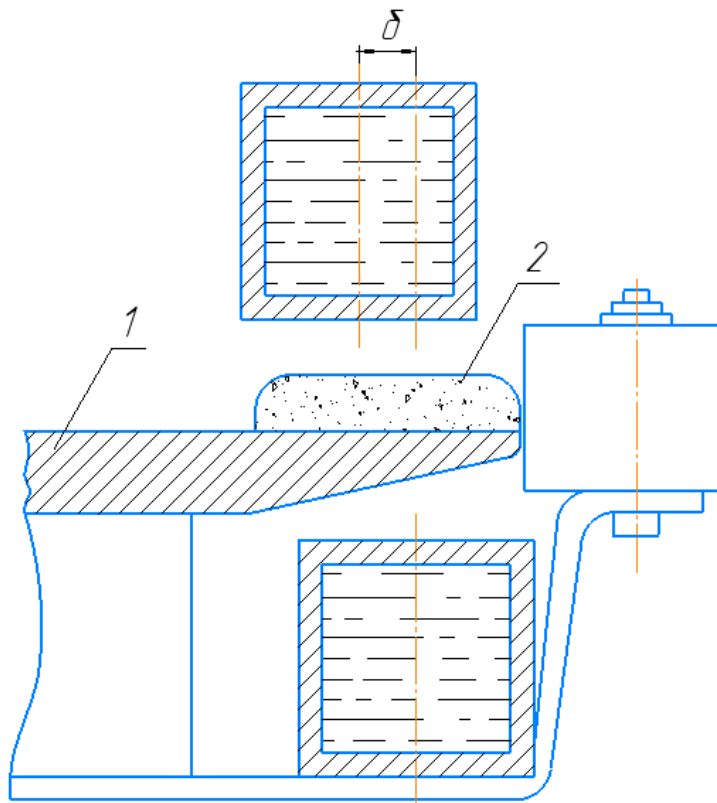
Положення лапи культиватора в індукторі при наплавлюванні: 1- деталь; 2- шар шихти [8 ст.151]
